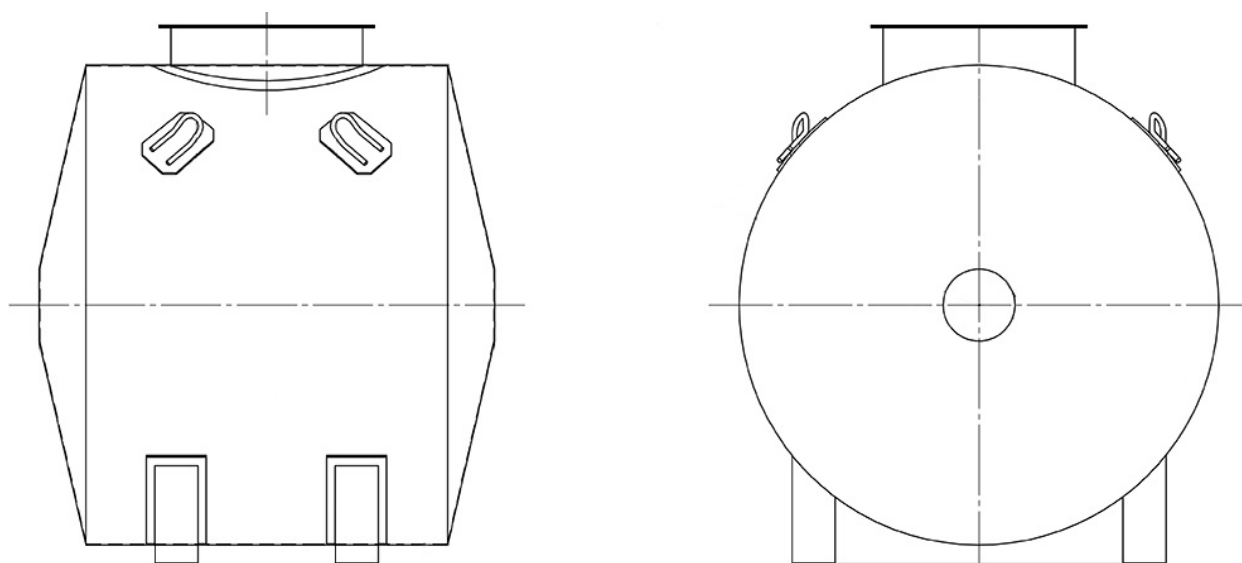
Общий вид резервуаров Р-БХТ 5/1/1-02
